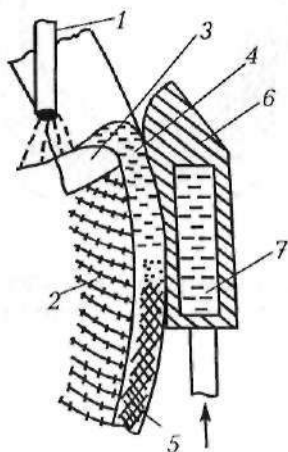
Схема процесса сварки с принудительным формированием шва:
